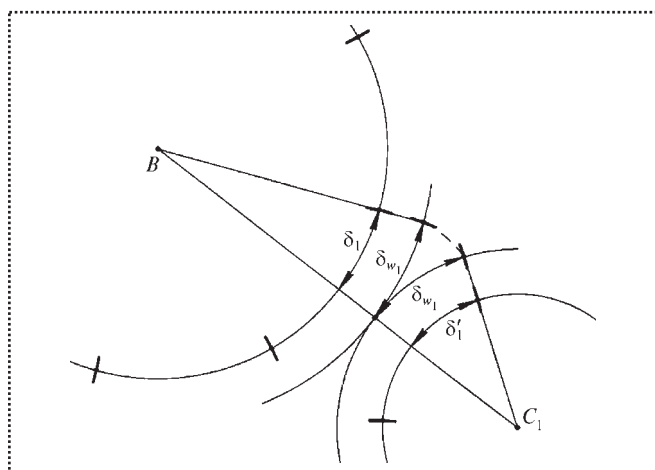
Расчетная схема условия сборки колес со смещением инструмента
